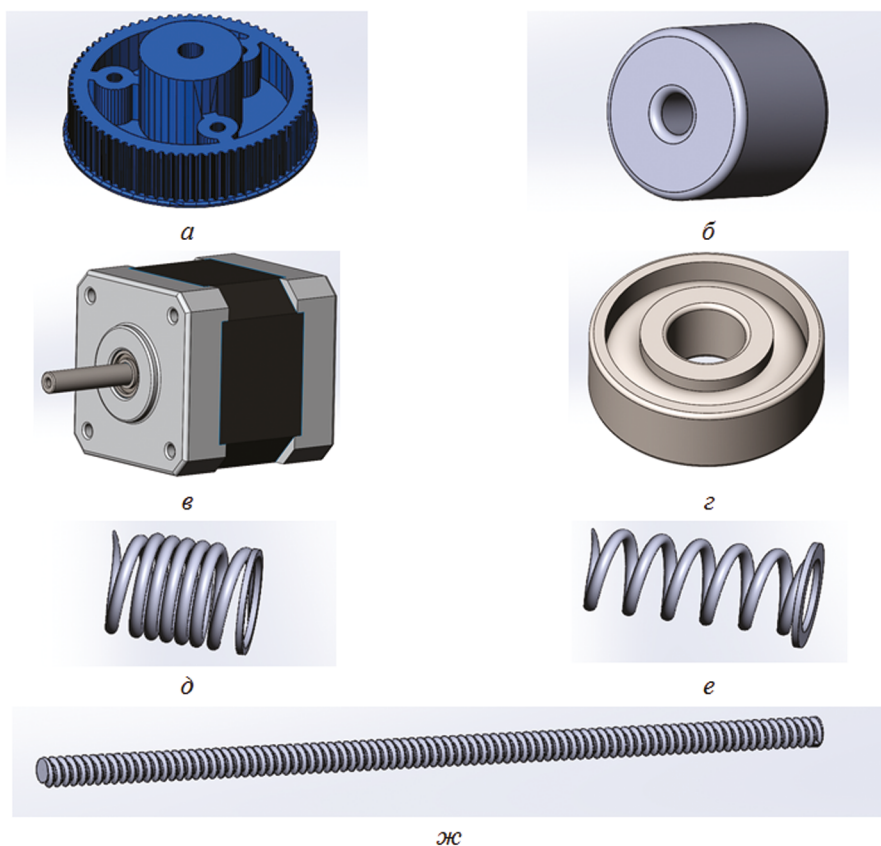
3D-модели элементов: *а* — ведомая шестерня; *б* — колесо полиуретановое; *в* — шаговый двигатель; *г* — подшипник; *д* — пружина в сжатом состоянии; *е* — пружина в разжатом состоянии; *ж* — шпилька резьбовая
